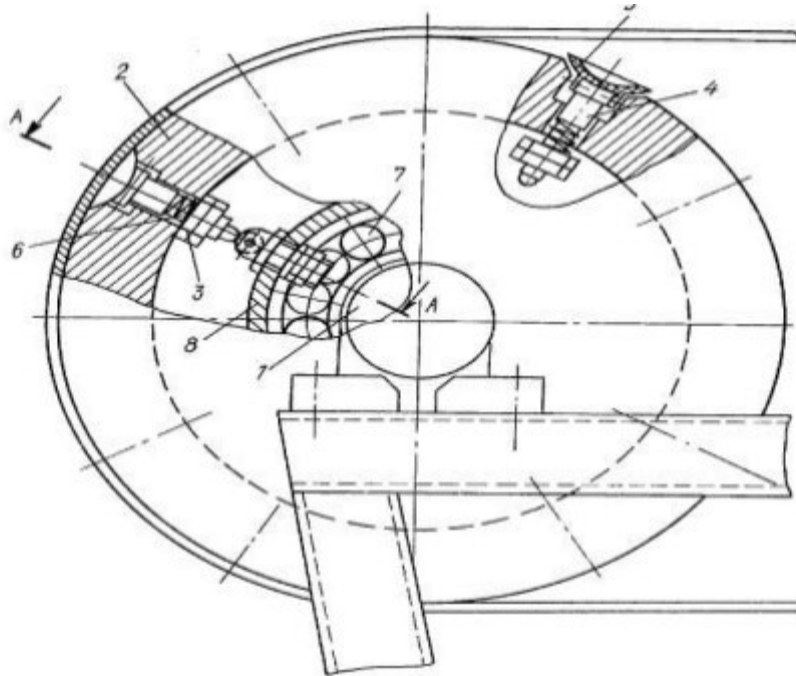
Схема дії приводного барабану стрічкового конвеєра
